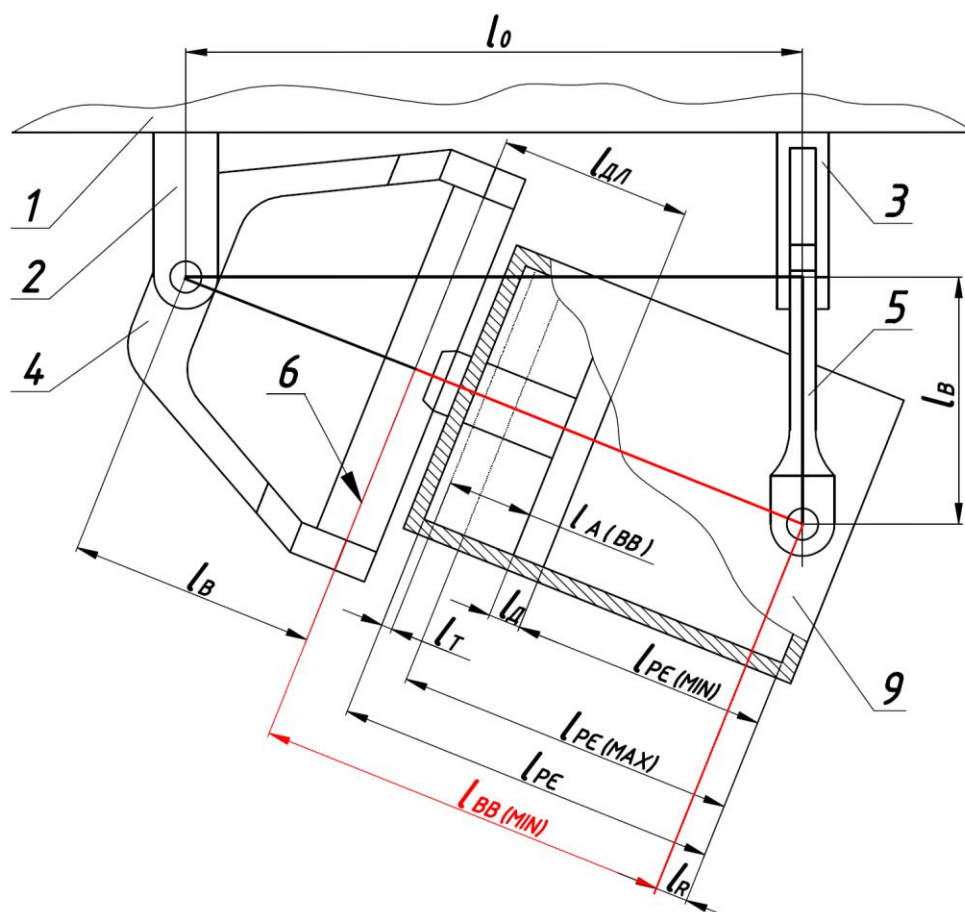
Розроблена машина для обробки деталей – вид зверху
